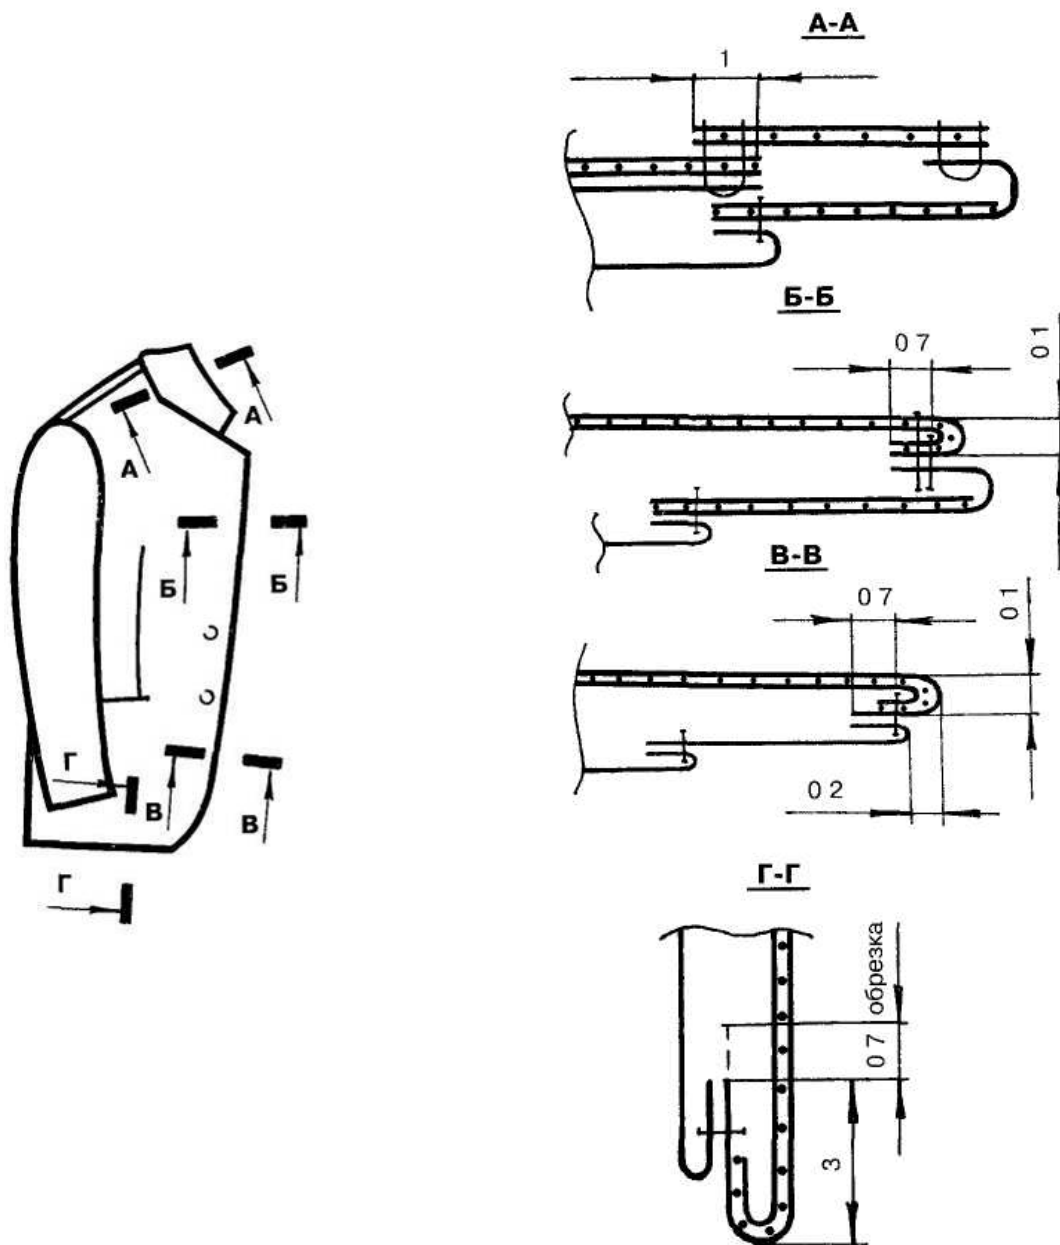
Сборочный чертеж узлов мужского пиджака
